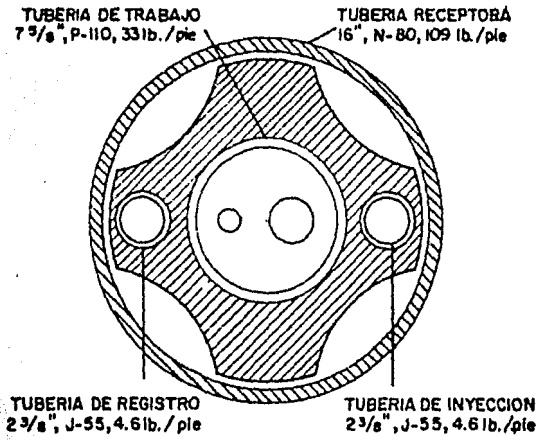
CORTE EN PLANTA DE LA ZAPATA
